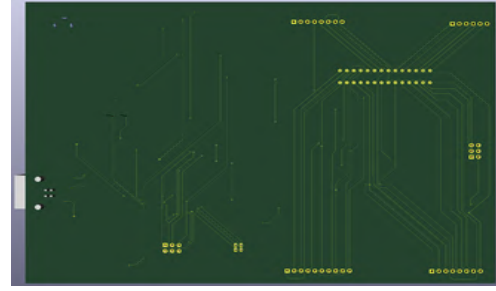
PCB tasarım 3B görüntüleme alt katman
